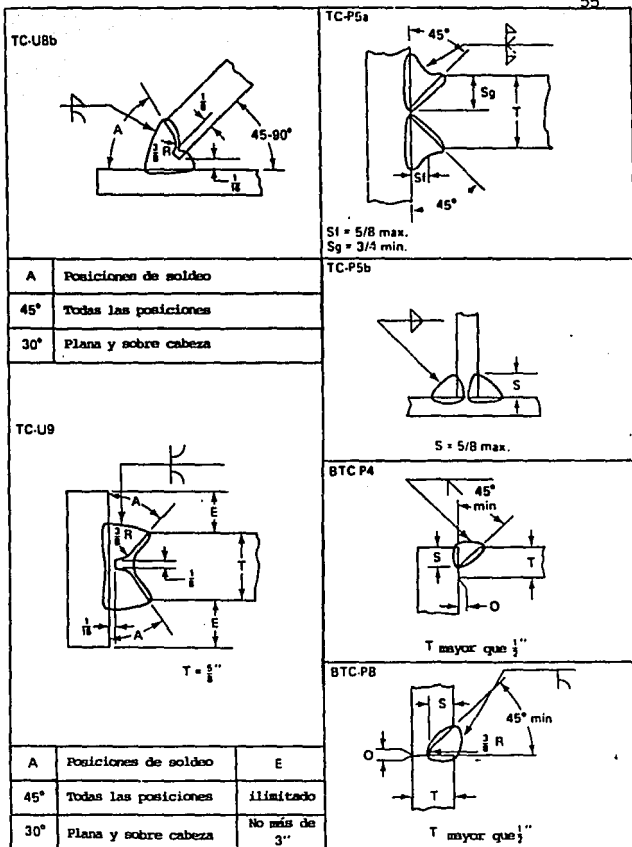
Diseño de uniones soldadas (cont.).
